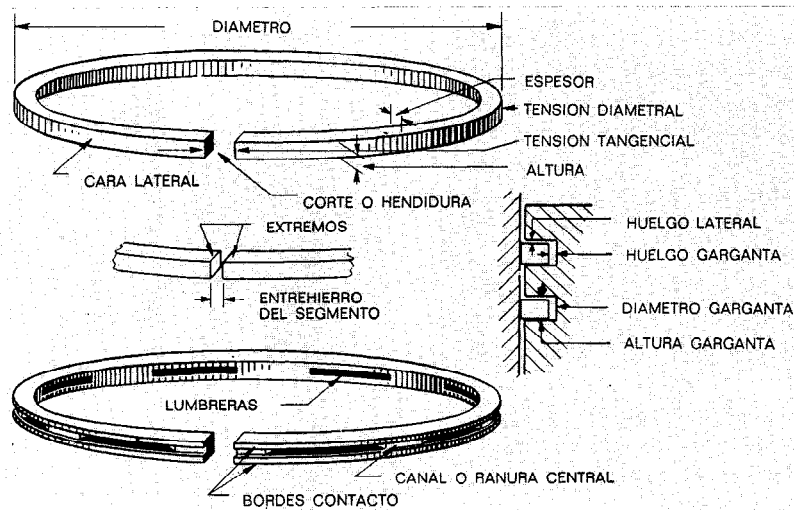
Segmento de compresión (arriba) y segmento de engrase (abajo) (*Sealed Power Corporation*).
